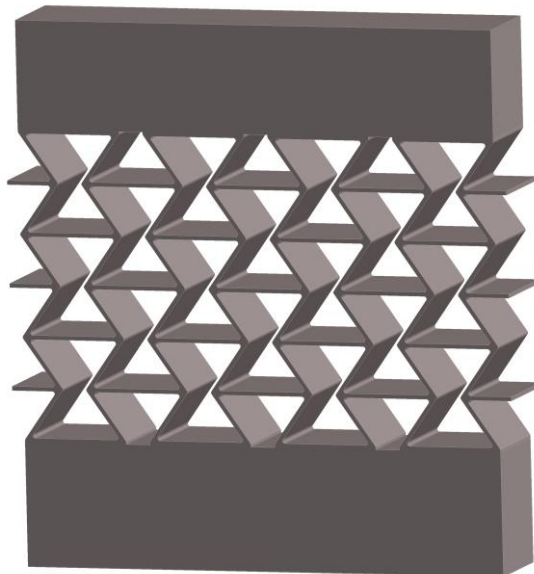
Upnutí vzorku pro testování cyklickým zatěžováním v tlaku [34].
